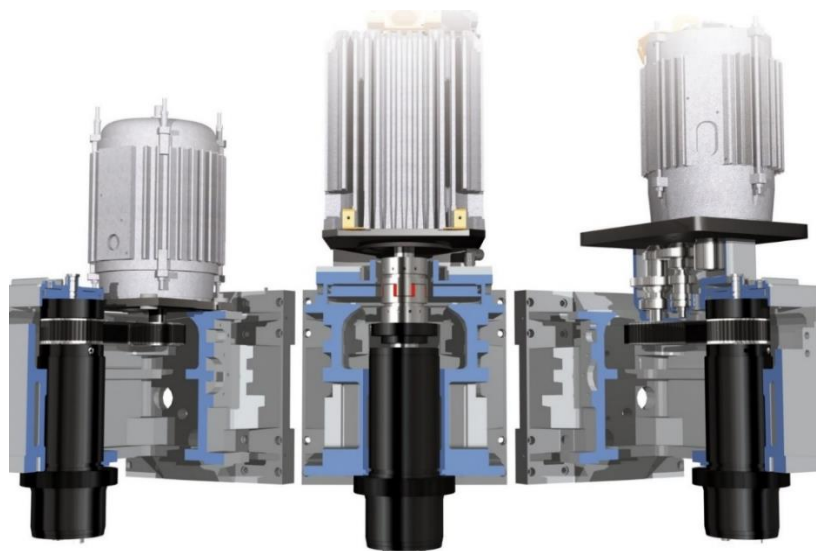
Приводи головного руху вертикально-фрезерних верстатів фірми HAAS Automation: а) прямий привод з пасовою передачею; б) прямий привод з пасовою передачею; в) привод з розширювальною коробкою швидкостей.
